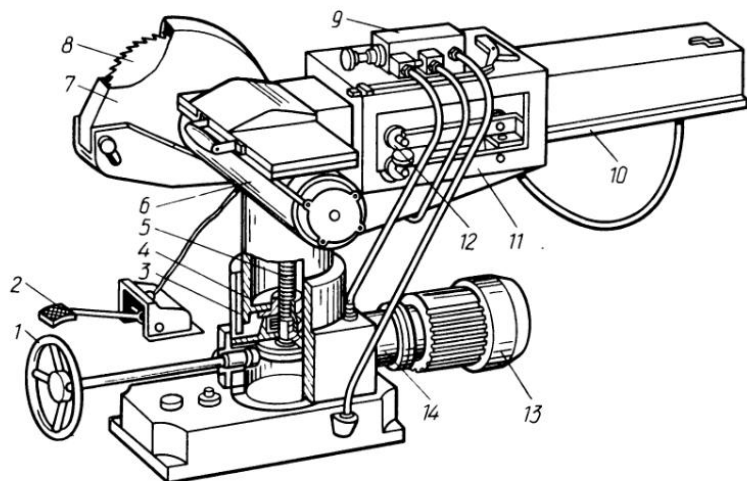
Круглопильный станок для поперечного раскря с прямолинейным перемещением суппорта ЦПА-2:
